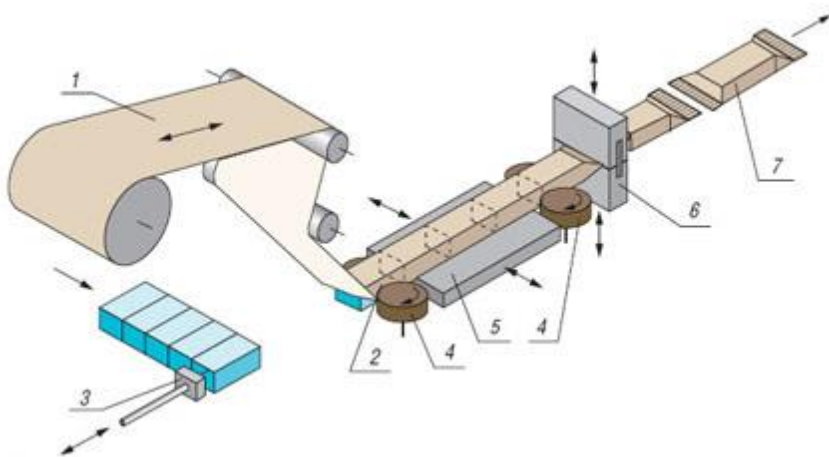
Схема дискретного технологічного процесу пакування штучних виробів в упаковку типу “флоу-пак”: 1 – пакувальний матеріал; 2 – рукав; 3 – штовхач; 4 – механізм протягування рукава; 5 – механізм поздовжнього зварювання; 6 – механізм поперечного зварювання і відрізання; 7 – готова продукція.
